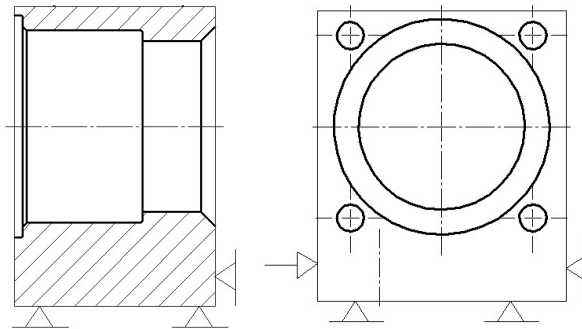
Схема базування деталі «Стійка А221.03»
